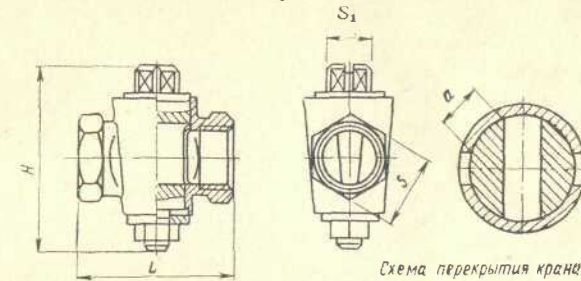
Конструкция крана натяжного пробкового для газопроводов
